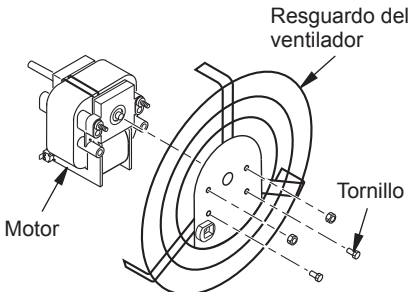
Desmontaje y montaje del resguardo del ventilador en el motor
